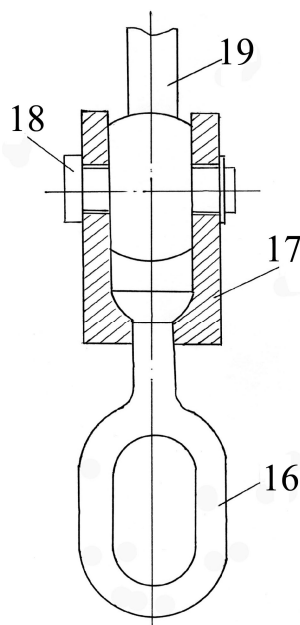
Шарнирный узел: 16 – серьга; 17 – обойма; 18 – палец; 19 – шток гидроцилиндра.
